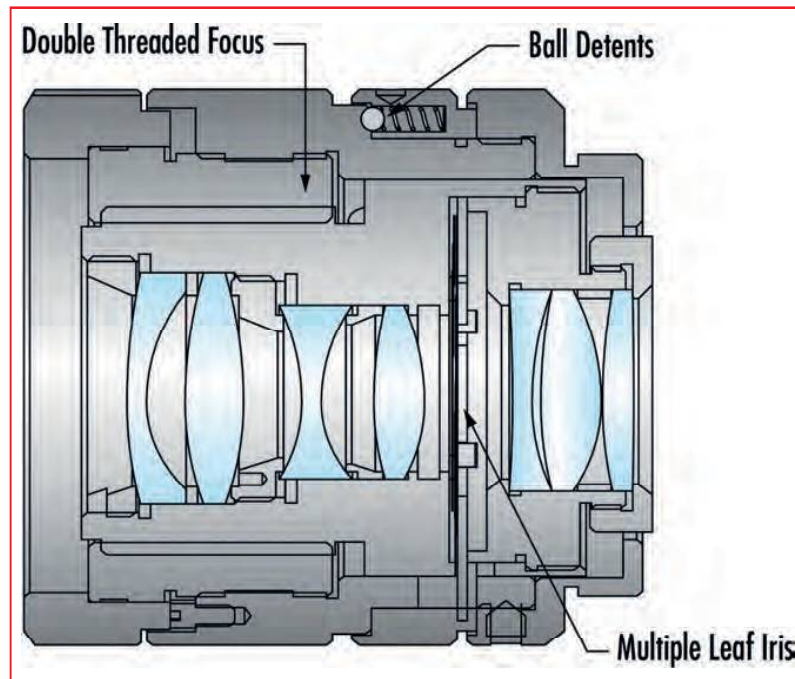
Sezione trasversale di una tipica lente a lunghezza focale fissa.
